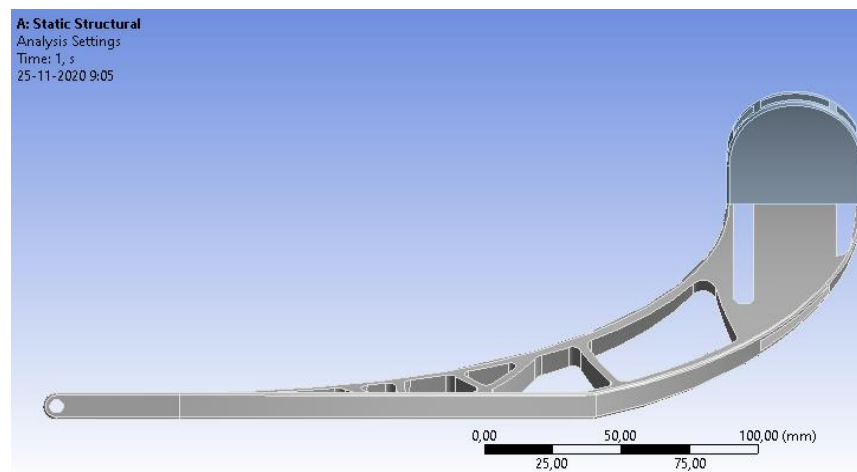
Vista 4 rediseño N°2 de eslabón pierna izquierda.
